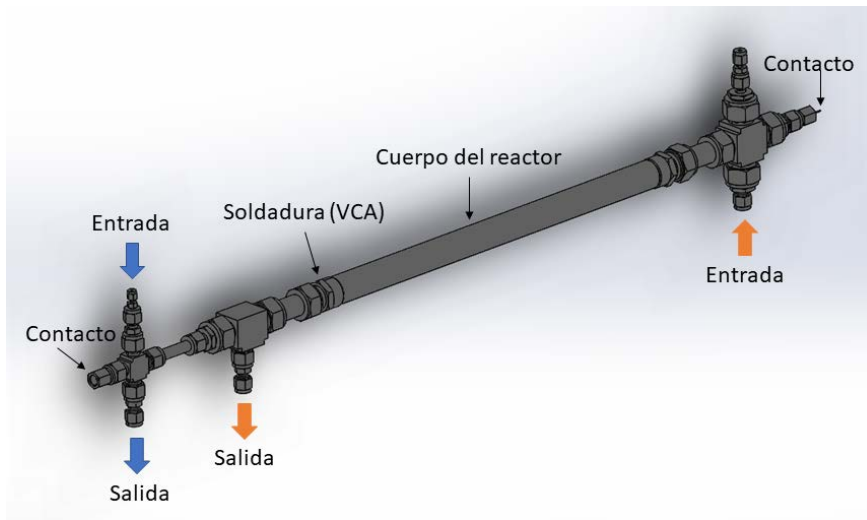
Vista isométrica del montaje de reactor de membrana de alta presión.
